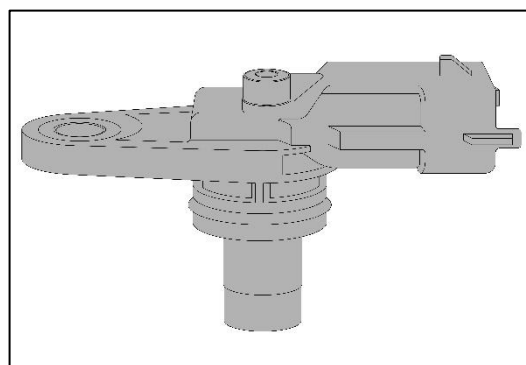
CAPTEUR D'ARBRE À CAMES
